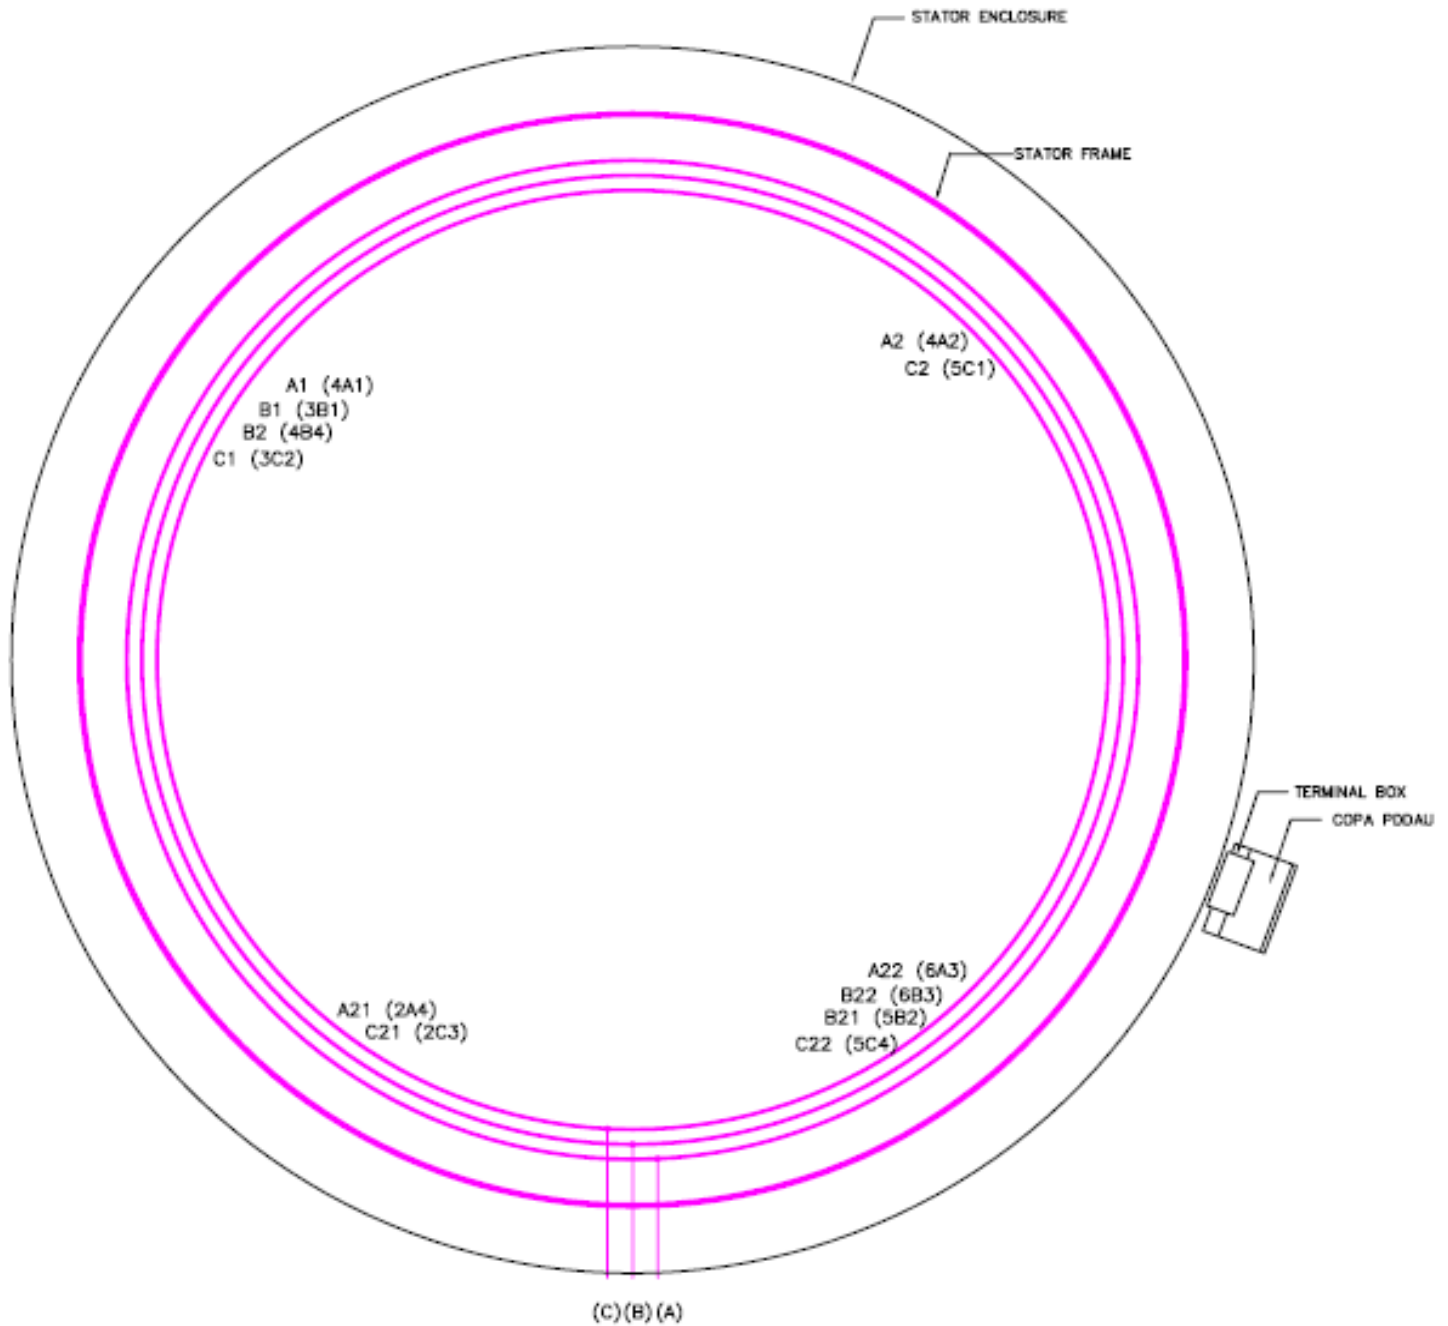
Posición de Puntos de Soldadura en Estator
